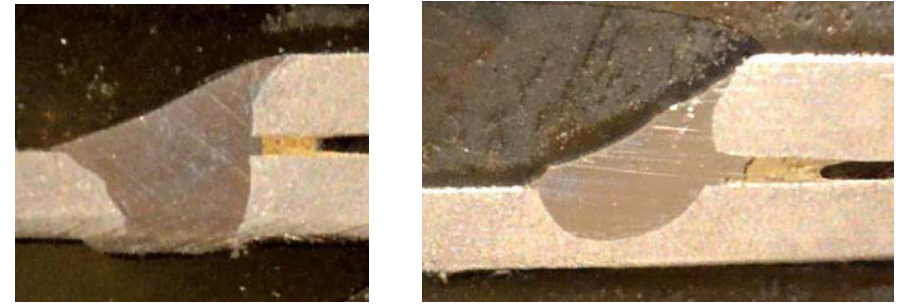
Макрошліфи паяно-зварних з'єднань
